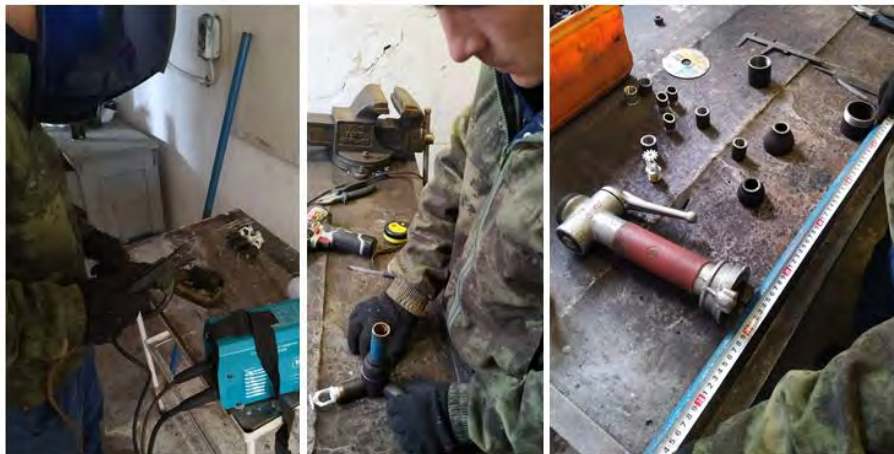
процесс сварочных работ и работ по примерке предполагаемых деталей, а так же подгонка деталей под предполагаемый ручной пожарный ствол
